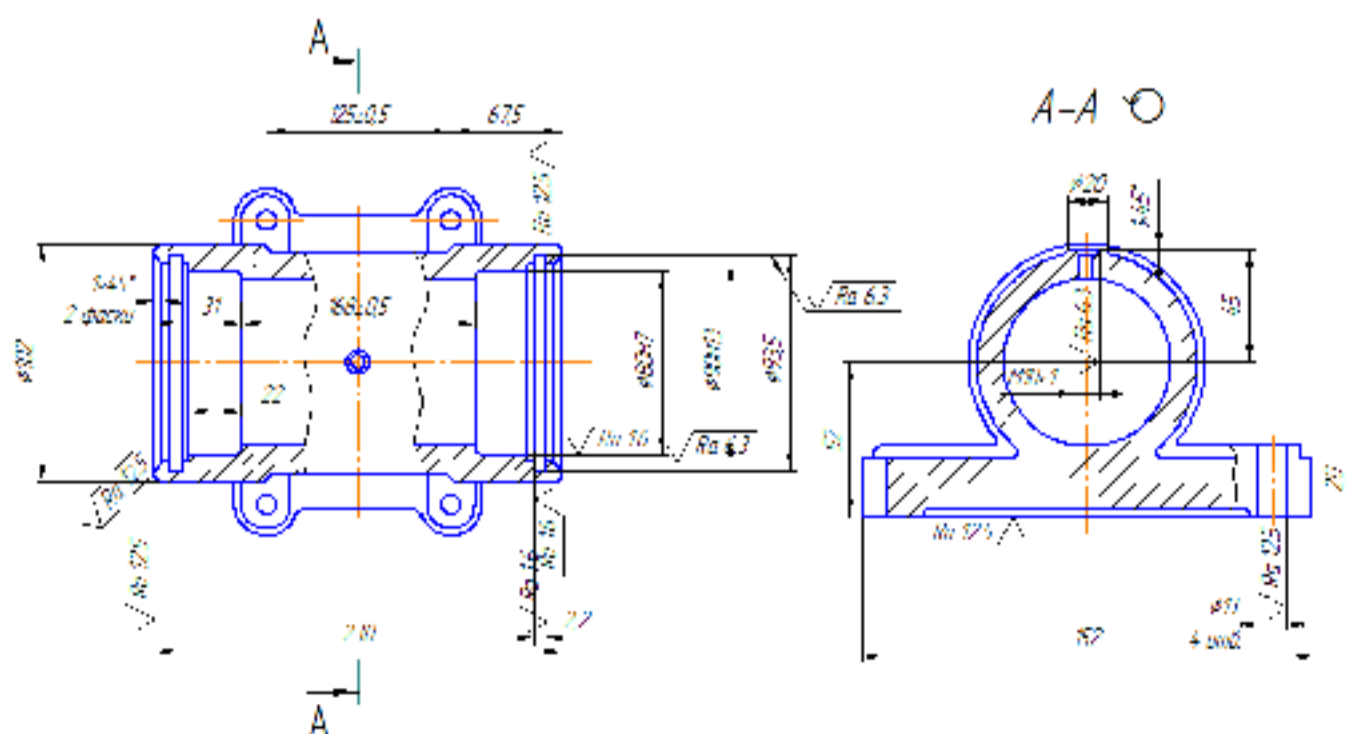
Поверхні деталі «Корпус підшипника 04.15.008В»
